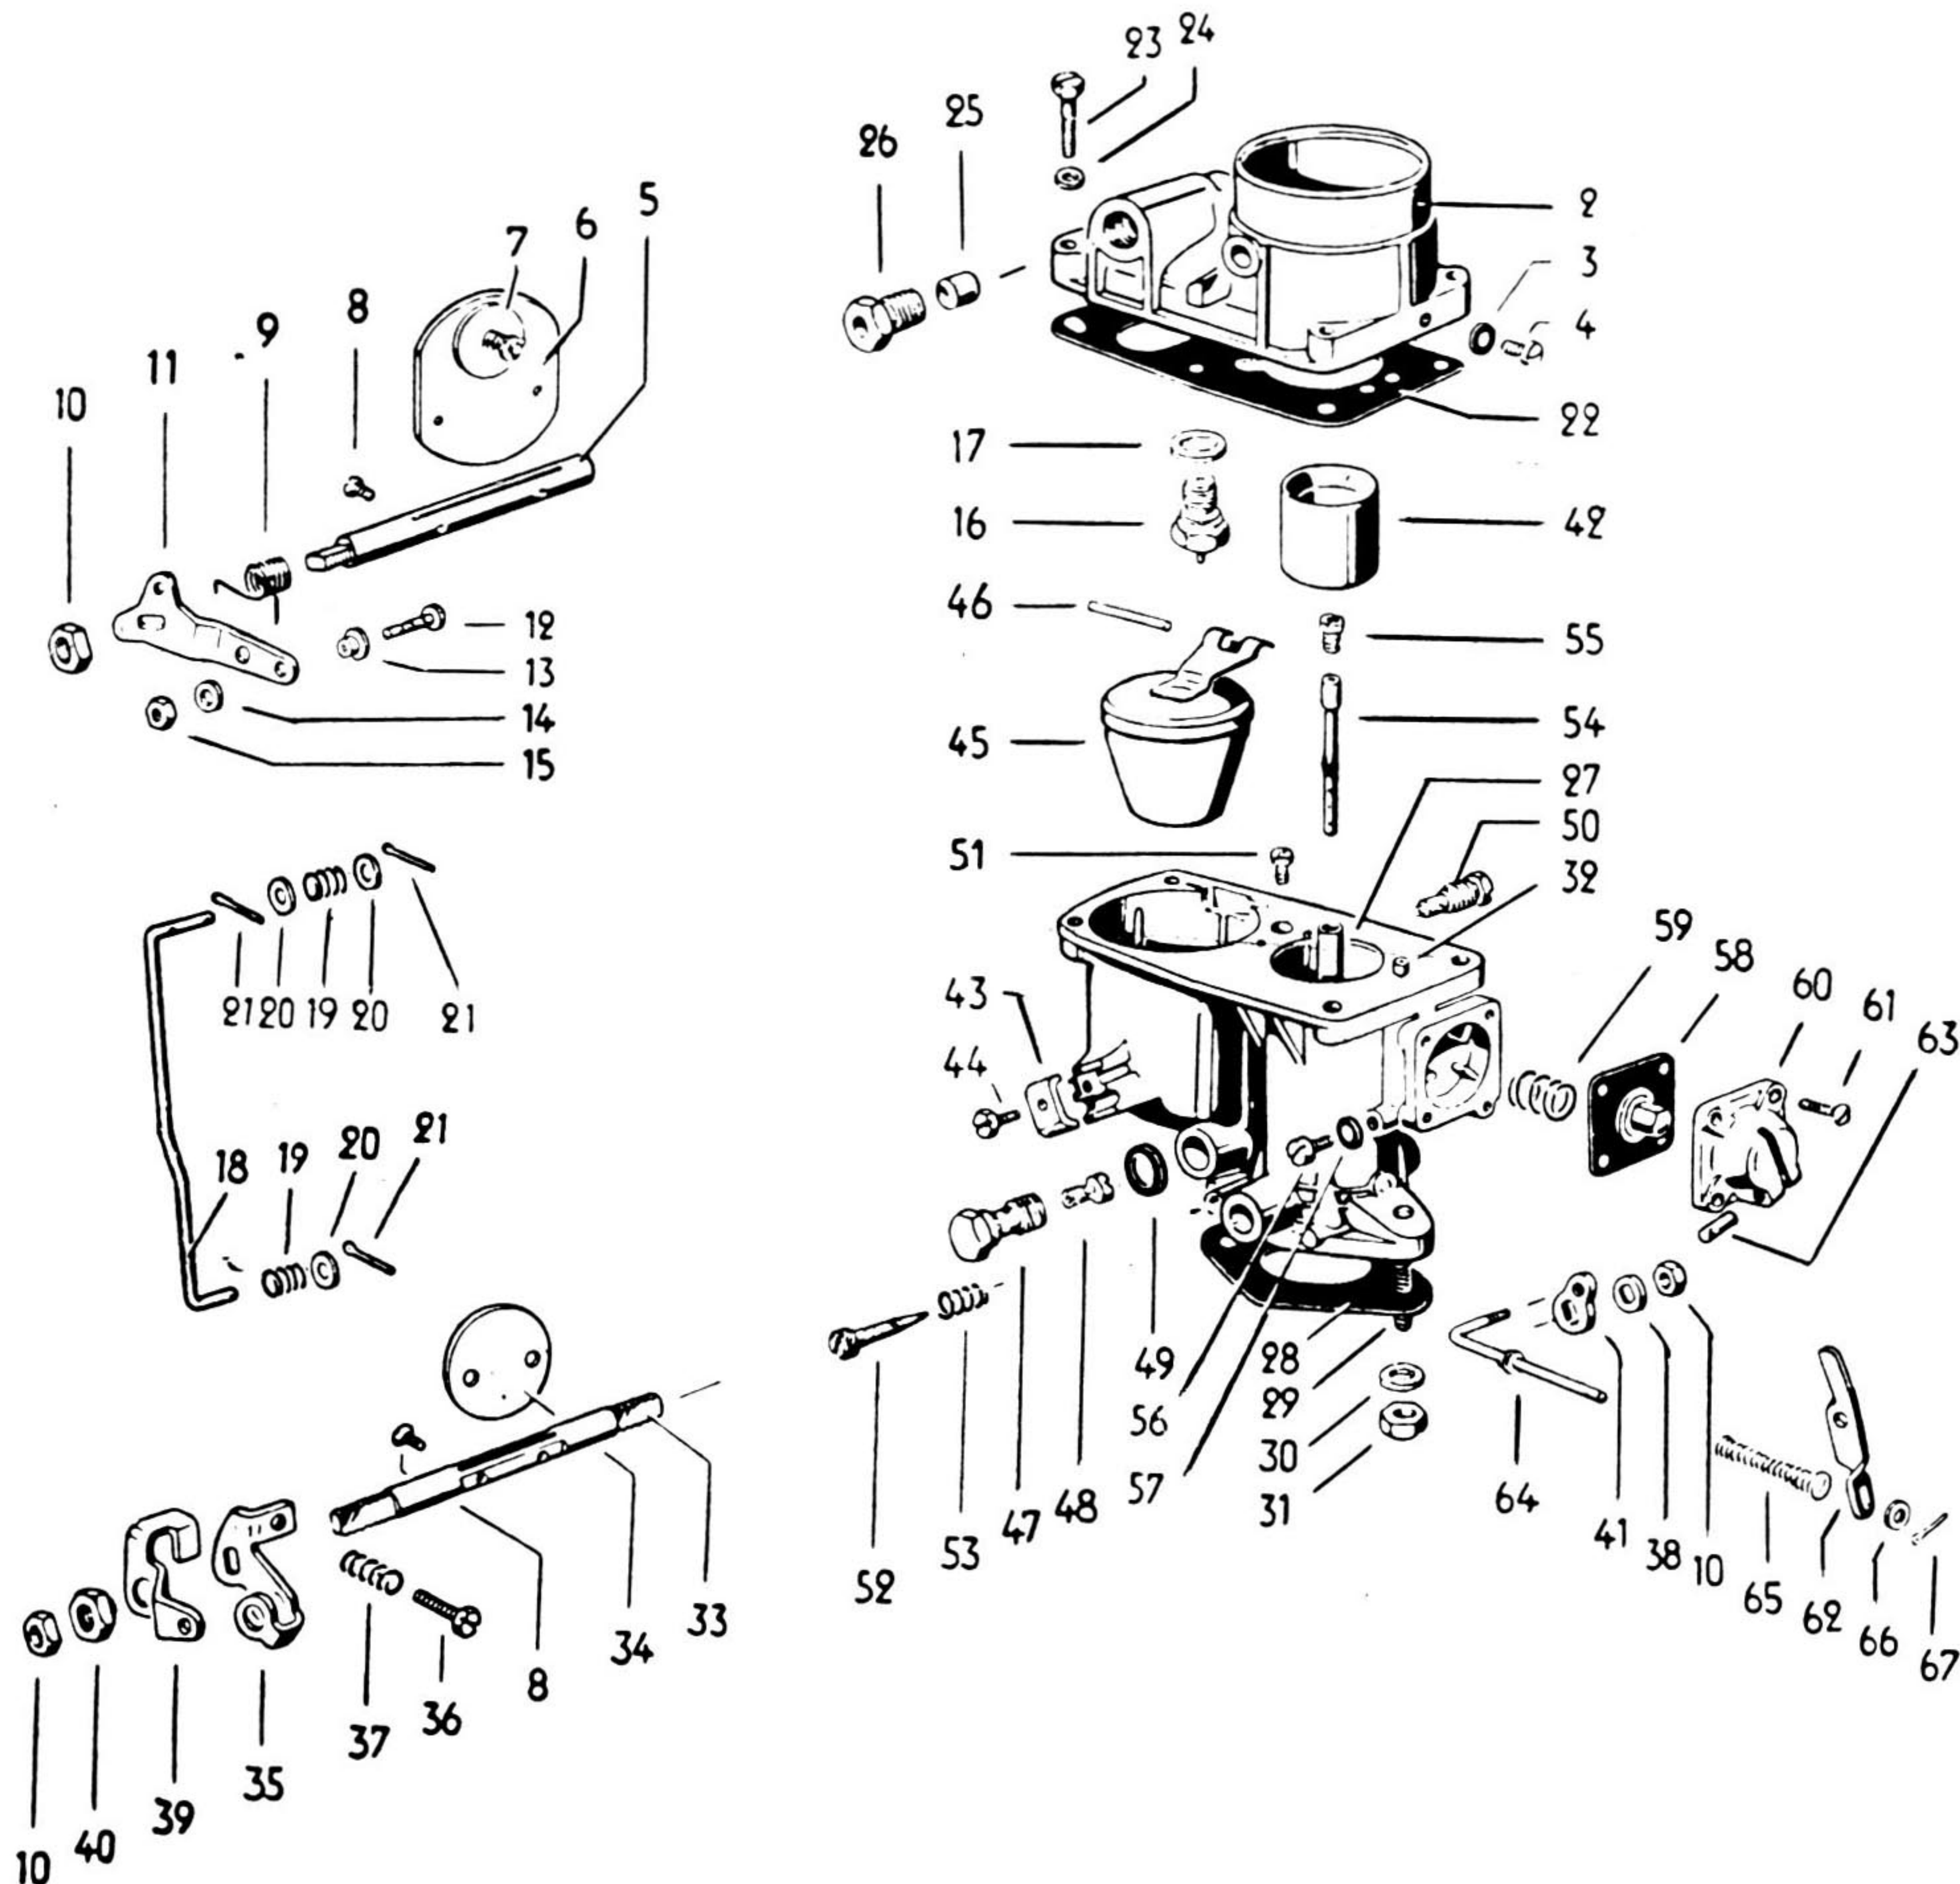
E — O carburador inteiramente desmontado. (Motor “1 200” — 36 HP)
